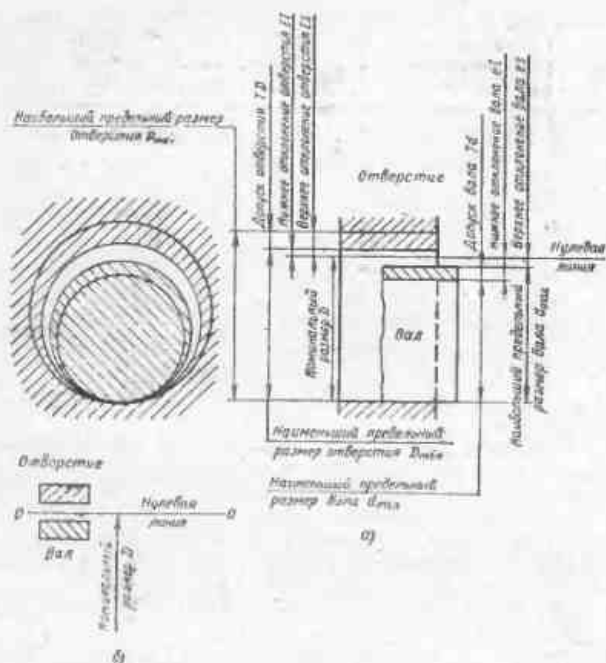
Расположение полей допусков отверстия и вала при посадке с зазором (оба отклонения отверстия положительны)
